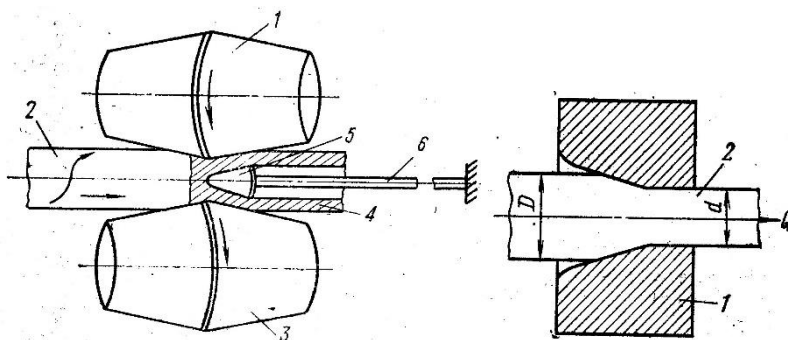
Схема кривой (винтовой) прокатки (вид сверху): 1-правый валок; 2-заготовка; 3-левый валок; 4- гильза; 5-оправка; 6-штанга (стержень)
